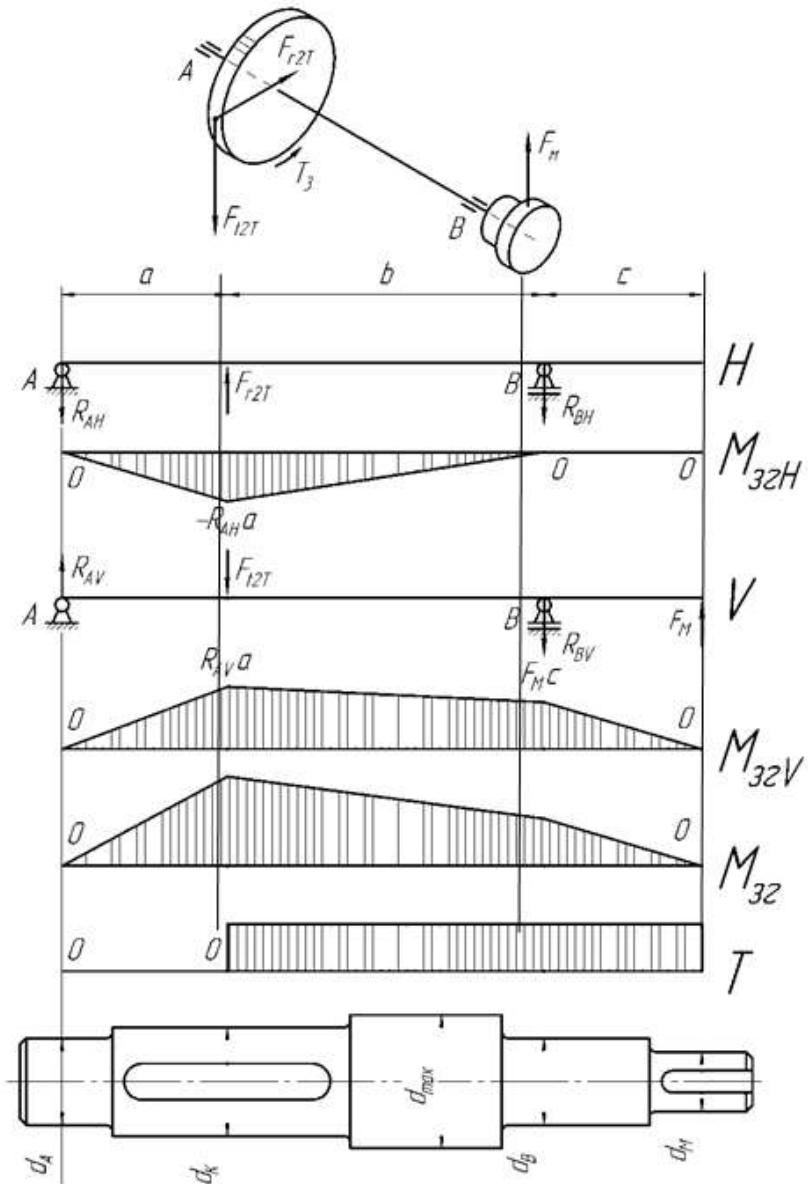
Розрахункова схема, епюри моментів і ескіз веденого вала циліндричного двоступінчастого редуктора
